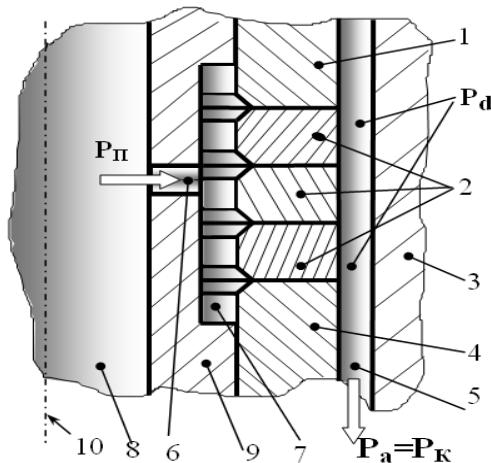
Фрагмент цилиндропоршневой группы компрессора с псевдопористой поверхностью щелевых питателей газового подвеса с питанием через полость поршня:
